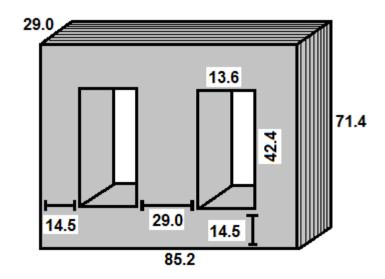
Núcleo do transformador. Dimensões geométricas em milímetro
